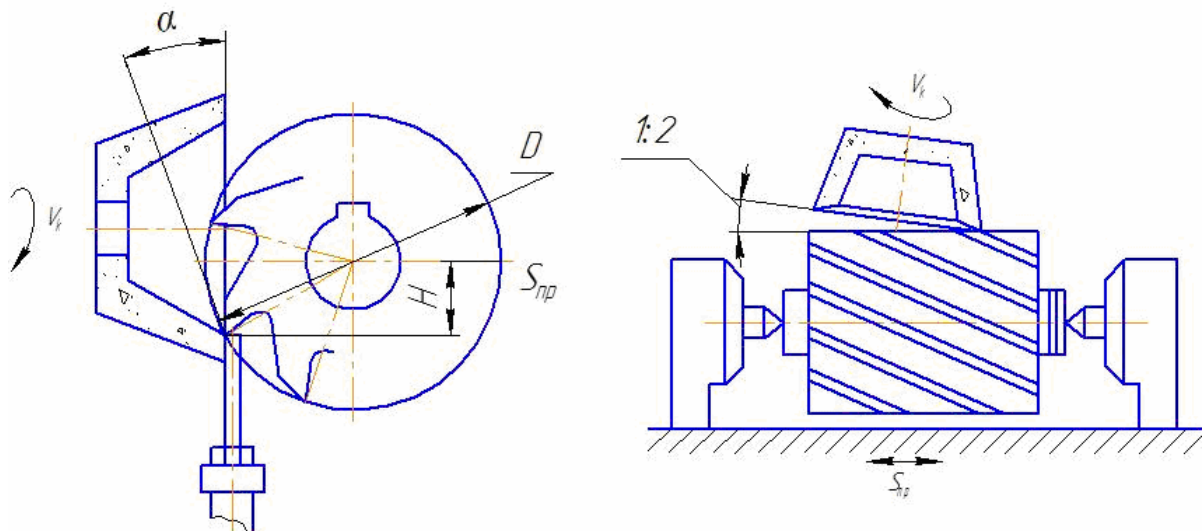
Схема заточування циліндричної фрези по задній поверхні
